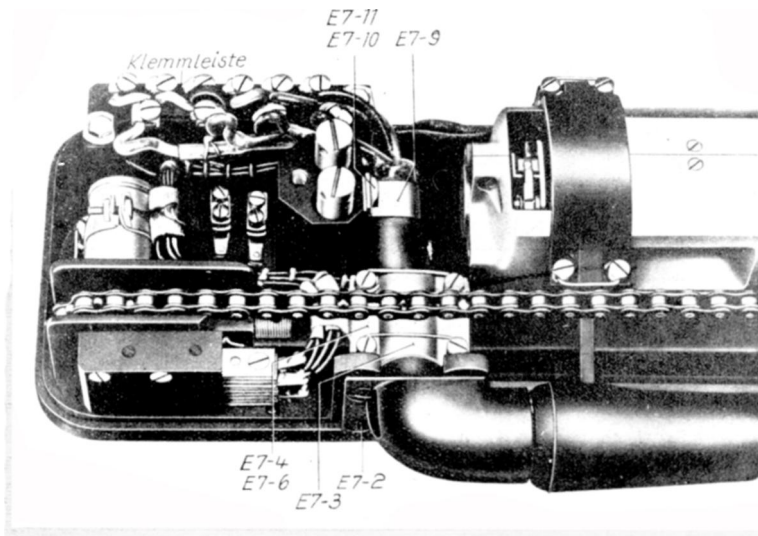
ED 151 B; Kabel; Befestigung und Anschluß
